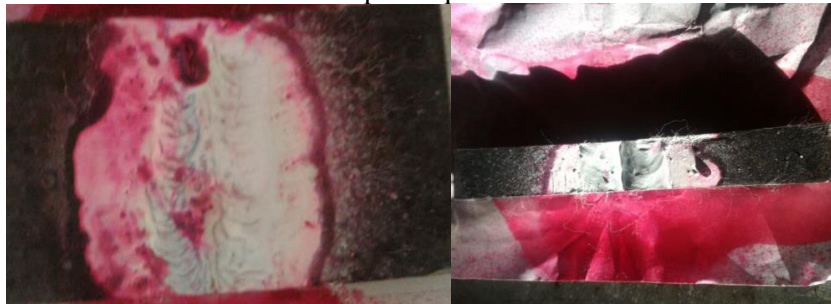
Junta Soldada. Fonte: Autorial Própria
